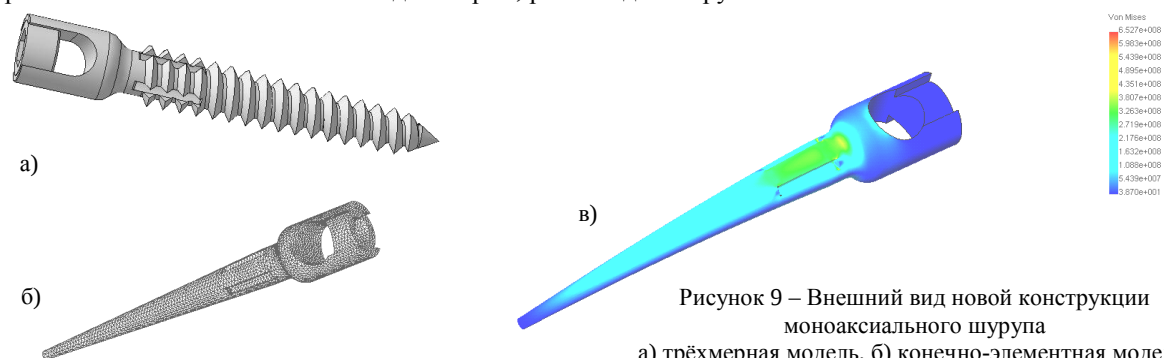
Внешний вид новой конструкции моноаксиального шурупа
